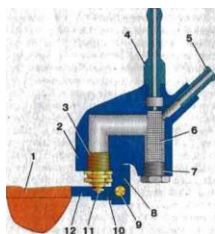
Схема поплавкового механизма и топливо-приемной системы карбюратора: 1 - поплавок; 2 - крышка карбюратора; 3 - топливный клапан; 4 - штуцер подачи топлива; 5 - штуцер слива топлива в бак; 6 - топливный фильтр; 7 - пробка; 8 - ограничитель хода поплавка; 9 - ось поплавков; 10 - язычок кронштейна; 11 - запорная игла топливного клапана; 12 - кронштейн поплавков
